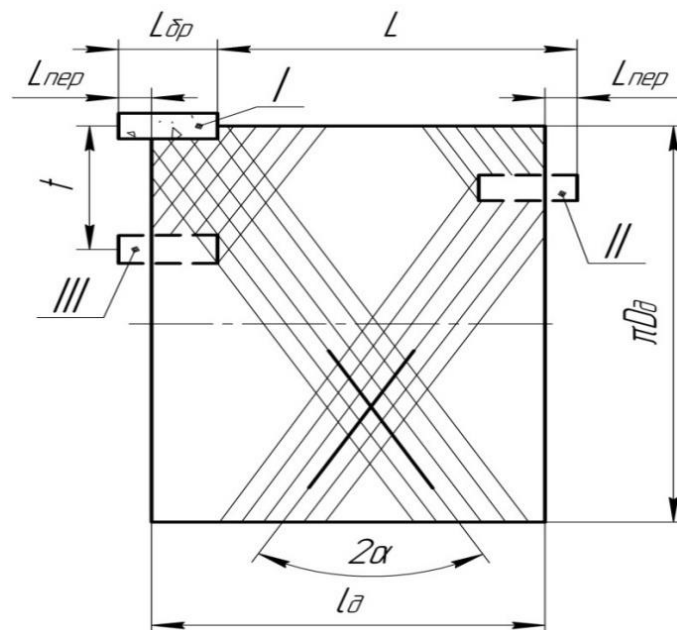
Сітка слідів обробки на поверхні деталі (розгортка):
